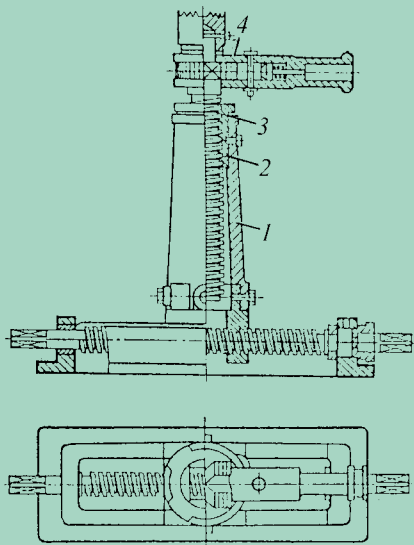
Схема винтового домкрата: 1 — литая станина; 2 — неподвижная гайка, по резьбе которой перемещается винт; 3 — стальной самотормозящий винт, заканчивающийся головкой; 4 — рукоятка с трещеткой
